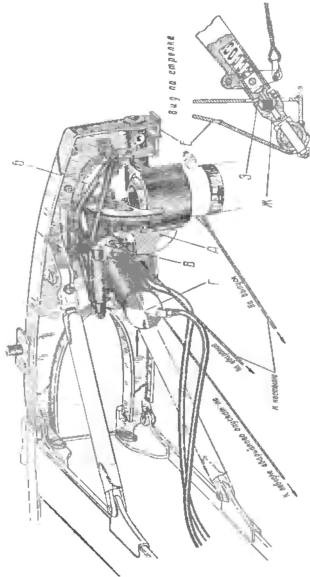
Механизм подъема и выпуска шасси (вид с внутренней стороны).
